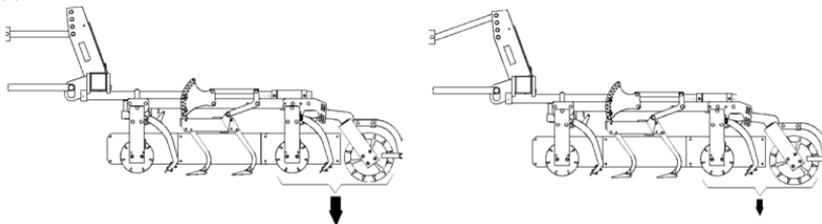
Регулировка давления на задний комкодробитель и разравнивающий каток
